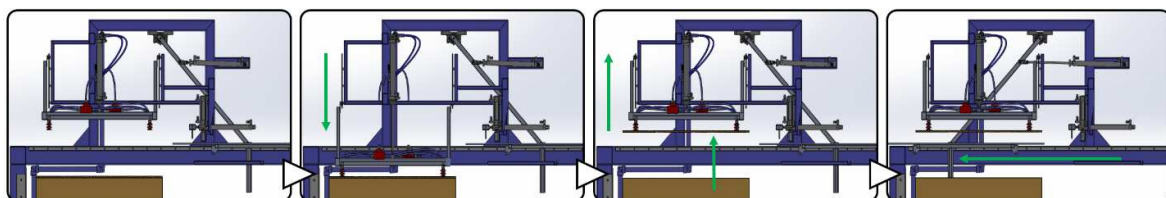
Elevación de la hoja (Sistema de Succión) y ubicación de la parrilla (Sistema de Apoyo).
